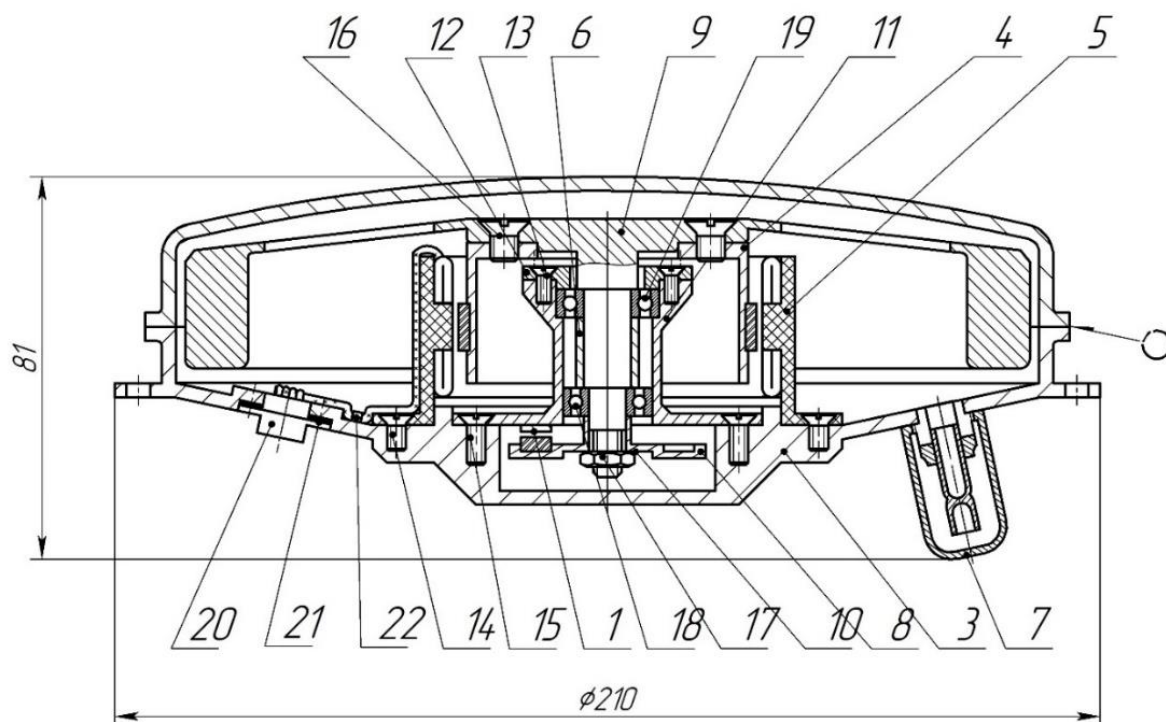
Фрагмент сборочного чертежа ИО, где
